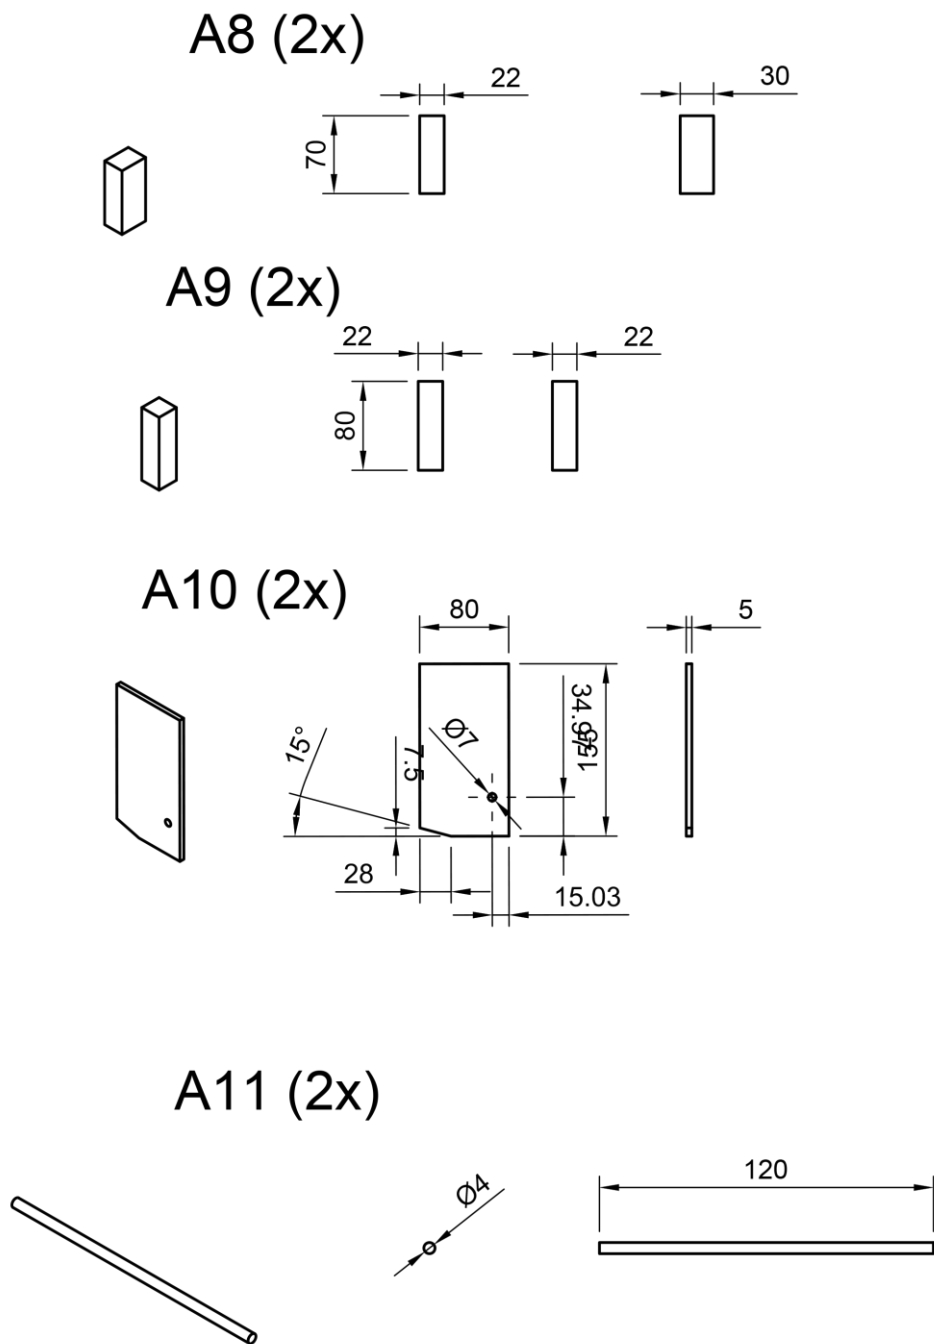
Ускоритель частиц – Детализированный вид - 4
